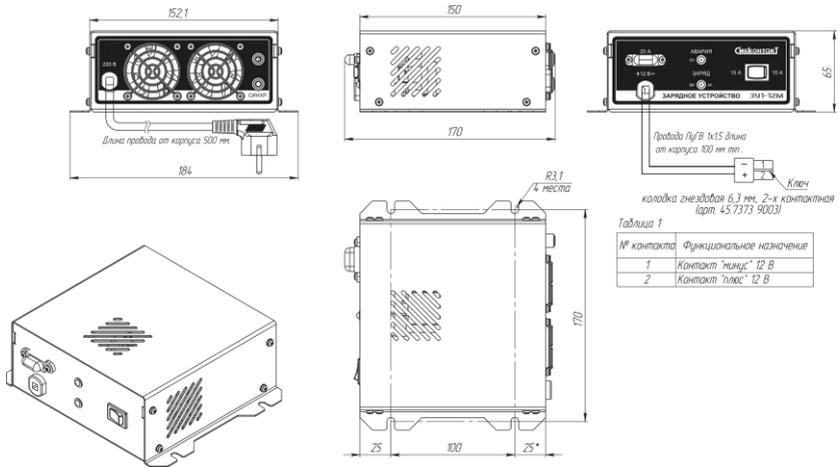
Внешний вид зарядного устройства ЗУ1-12M
